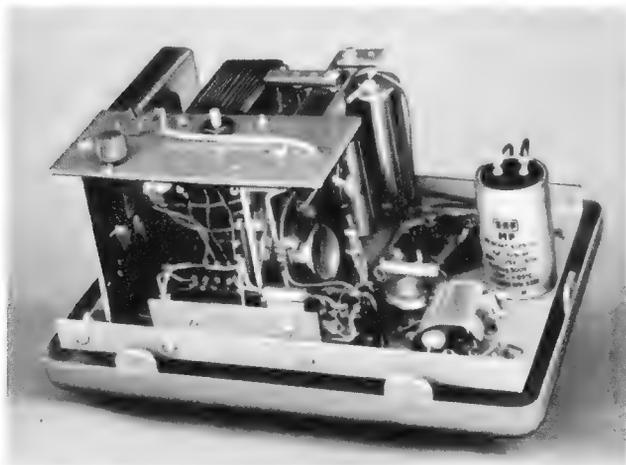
Der Aufbau und die Verdrahtung des Transistor-Modulators sind gut zu erkennen. Das Chassis wird von passenden Gewindebolzen auf Abstand von der Frontplatte gehalten. Für das Meßwerk ist im Chassis ein Ausschnitt ausgespart, Meßwerk und Buchsen sind an der Frontplatte befestigt, alle anderen Bauteile trägt das Chassis. Auf Maßskizzen für das Chassis wurde verzichtet, weil sich jeder Amateur nach vorhandenen Teilen richtet
